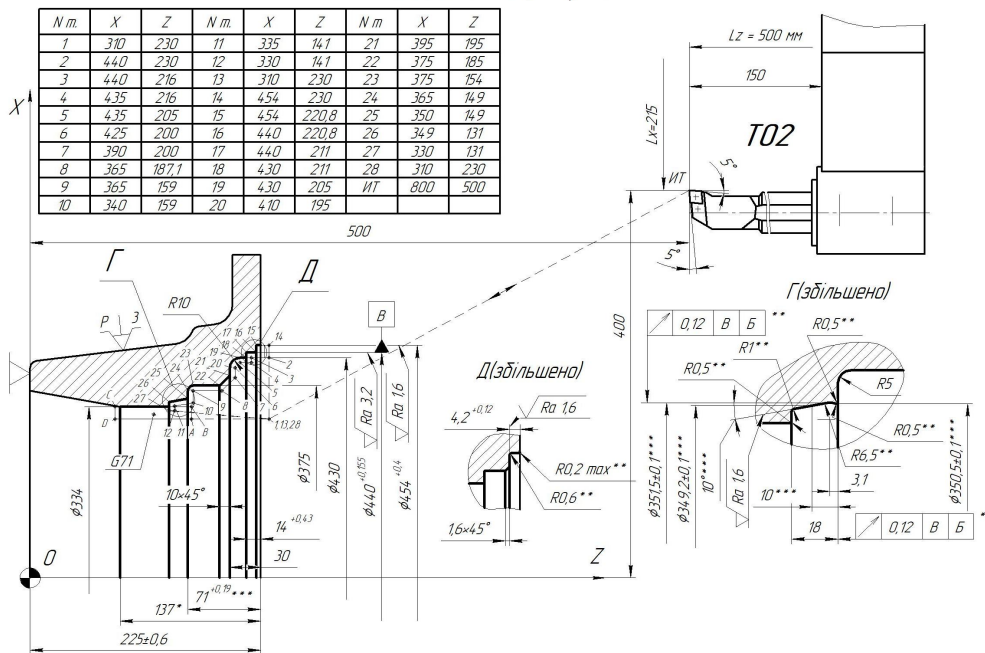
Установ А, перехід 2: схема обробки деталі та координатне розташування інструмента
